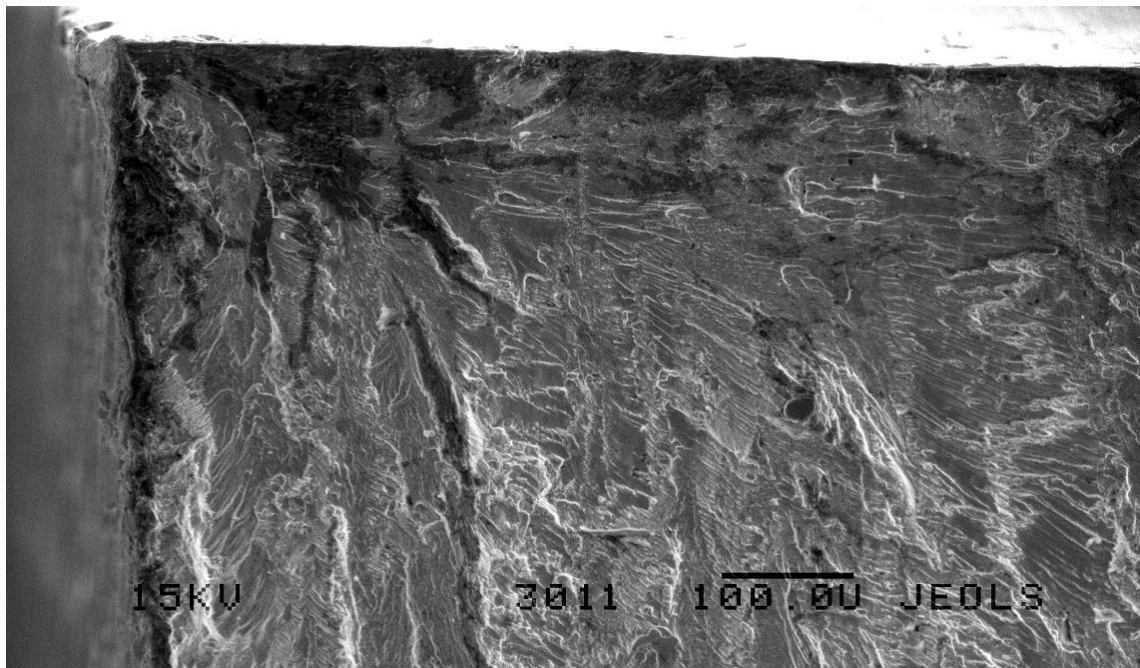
Излом образца с рисунка 3.48. Очаг зарождения усталостной трещины — скопление неметаллических включений, выходящее на образующую отверстия [122]
